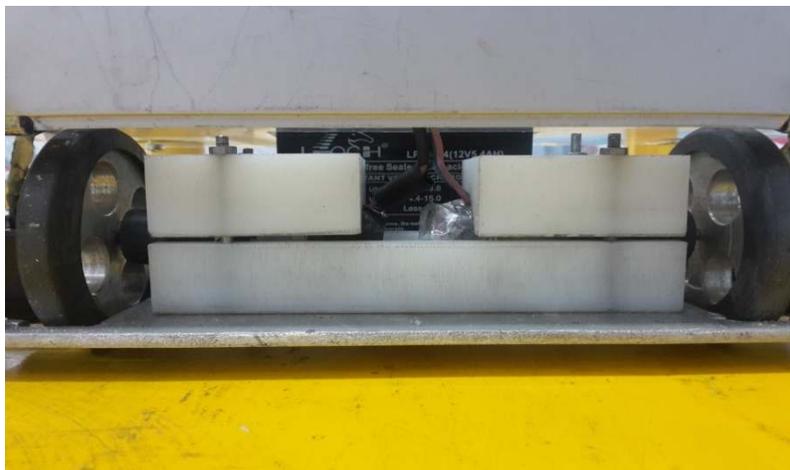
Roues fixées aux 2 moteurs sur le châssis
